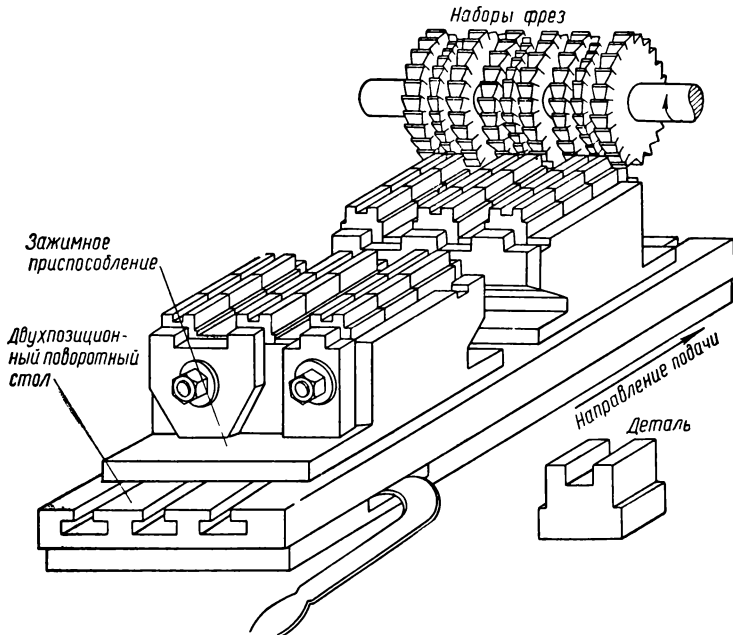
Фрезерование набором фрез в многоместном приспособлении
